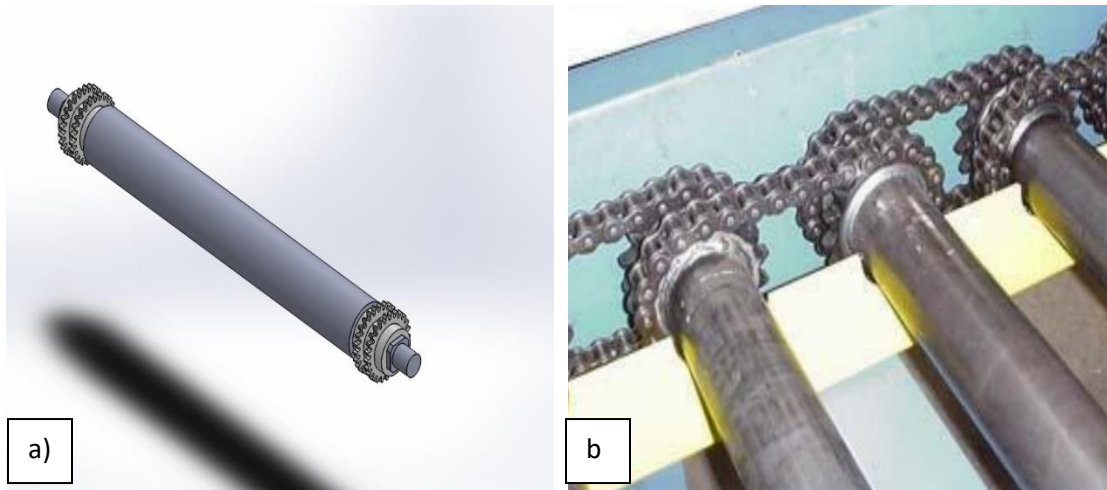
a) Ensamble rodillo piñón. b) Imagen de rodillos y piñón que se busca implementar.
